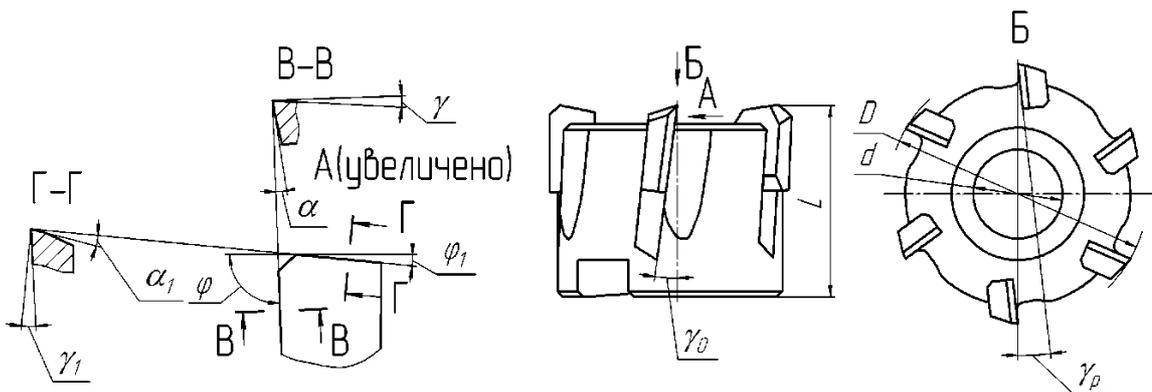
Эскиз торцевой фрезы со вставными ножами
